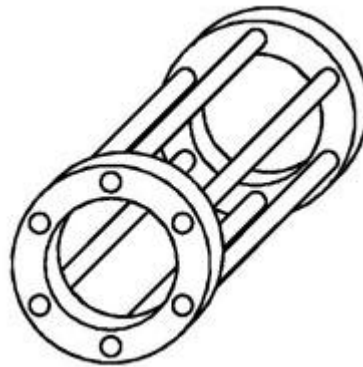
Rotor Jaula de Ardilla para un motor de inducción
